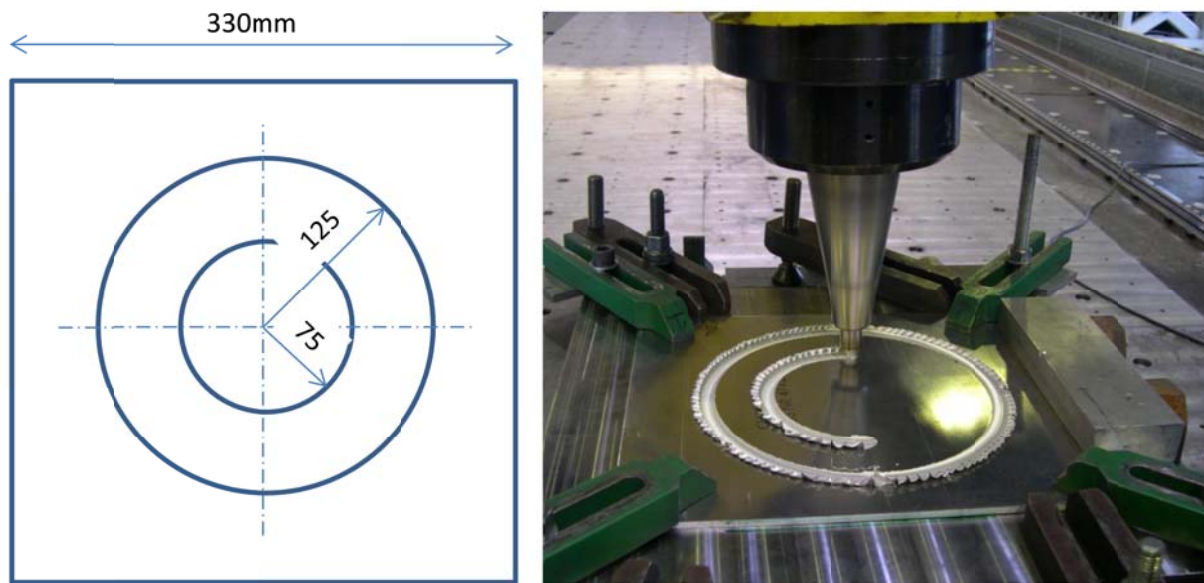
Photographie du dispositif expérimental pour les soudures circulaires
